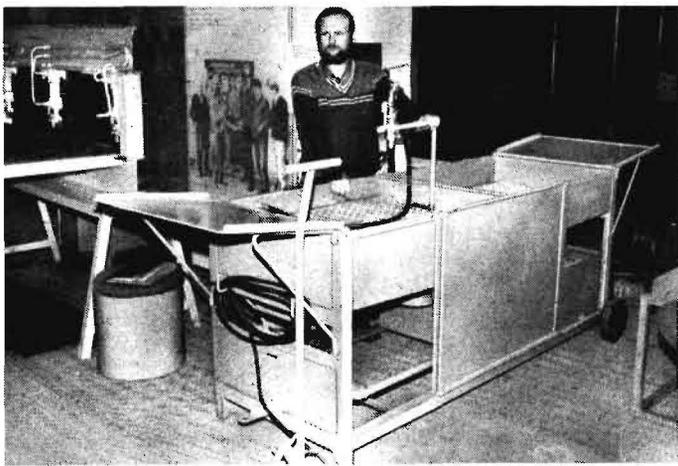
Waschanlage für Maschinenteile und Baugruppen
